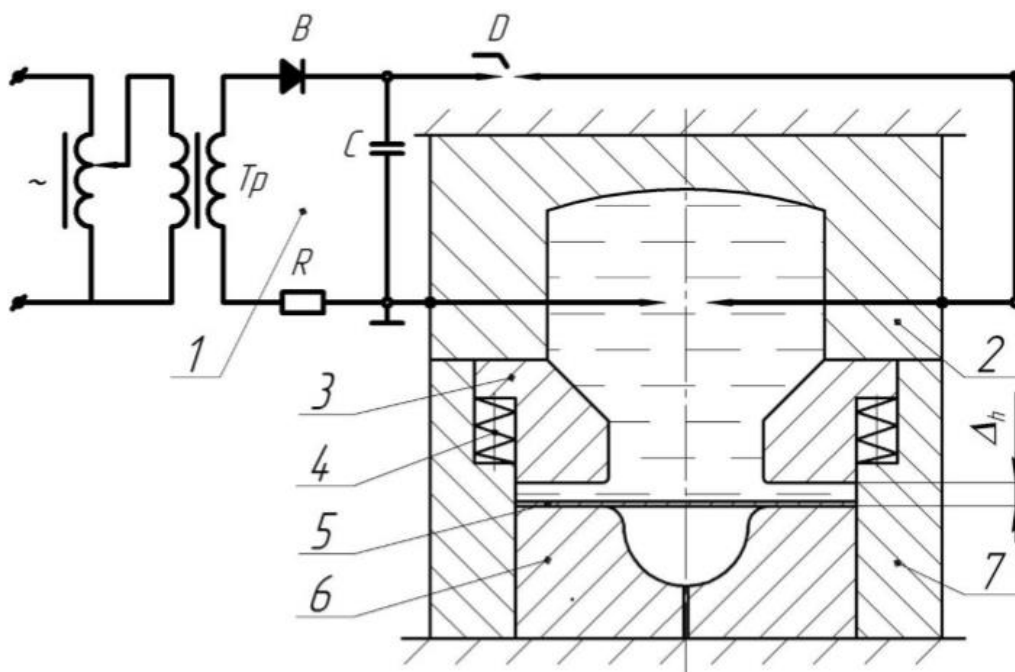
Схема інтенсифікованої ЕГД витяжки-формування з додатковим використанням ресурсу пластичності фланця заготовки: 1 – ЕГД-установка; 2 – розрядна камера; 3 – інерційний розгладжувач; 4 – пружний елемент; 5 – листова заготівля; 6 – формозмінювальна матриця; 7 – зовнішня обойма; D – розрядник; C – конденсаторна батарея; R – обмежувальний опір; Tг – трансформатор; Re – випрямляч
